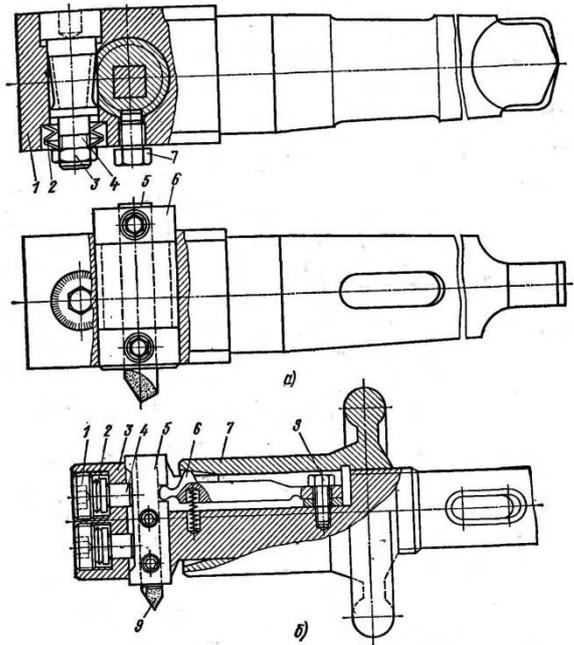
Регулируемая борштанга для растачивания отверстий: а — черновой, б — листового
